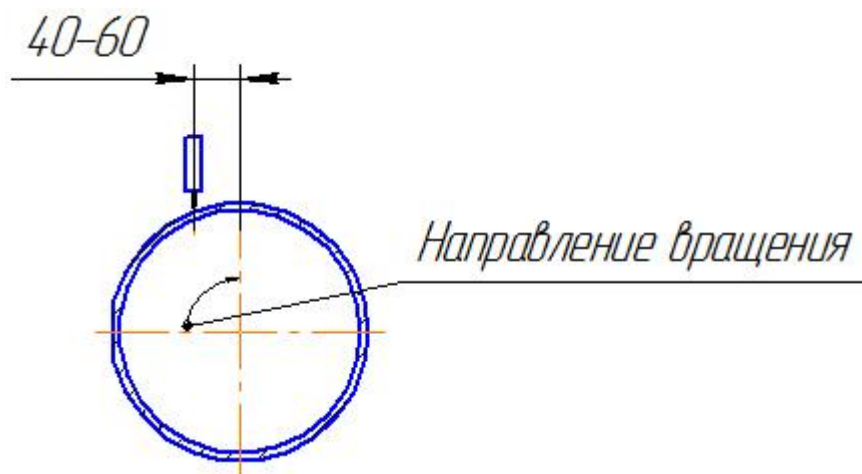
Положение электрода при сварке кольцевого шва снаружи
